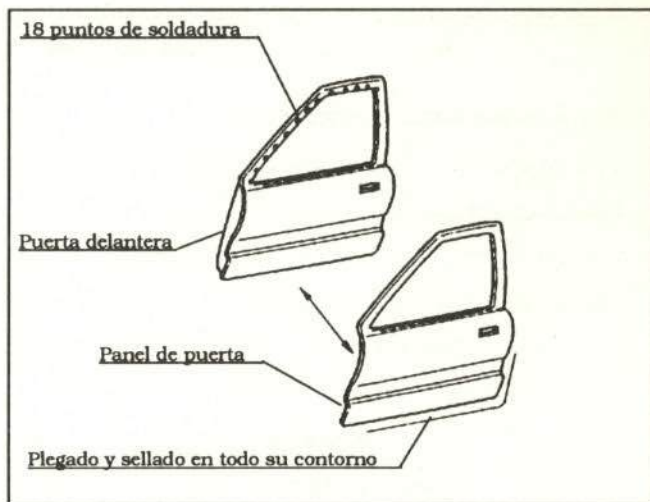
UNION DEL PANEL DE PUERTA CON SU ARMAZON
